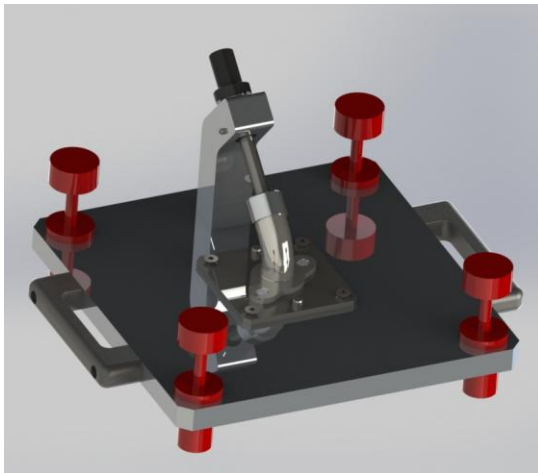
Utillaje de soldadura láser de tubo y brida de salida de gases.
